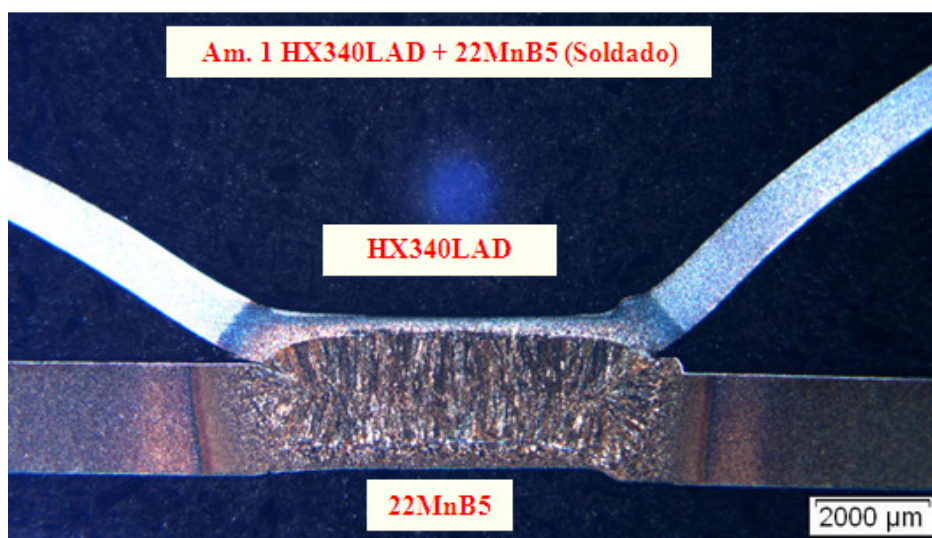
União soldada HX340LAD – TL4255 (20X).
